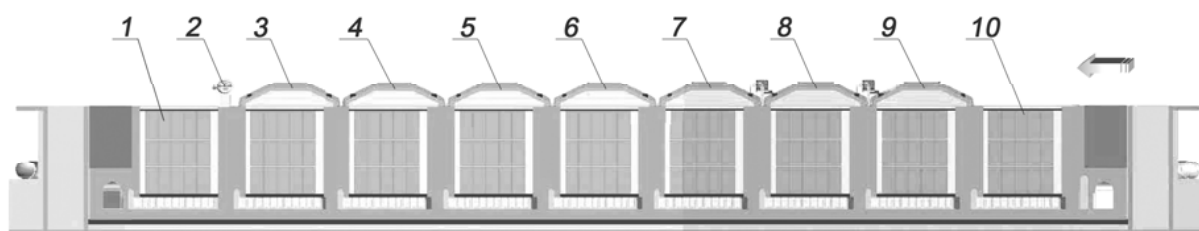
Схема випалювання заготовок у багатокамерній печі типу Рідгаммера:
